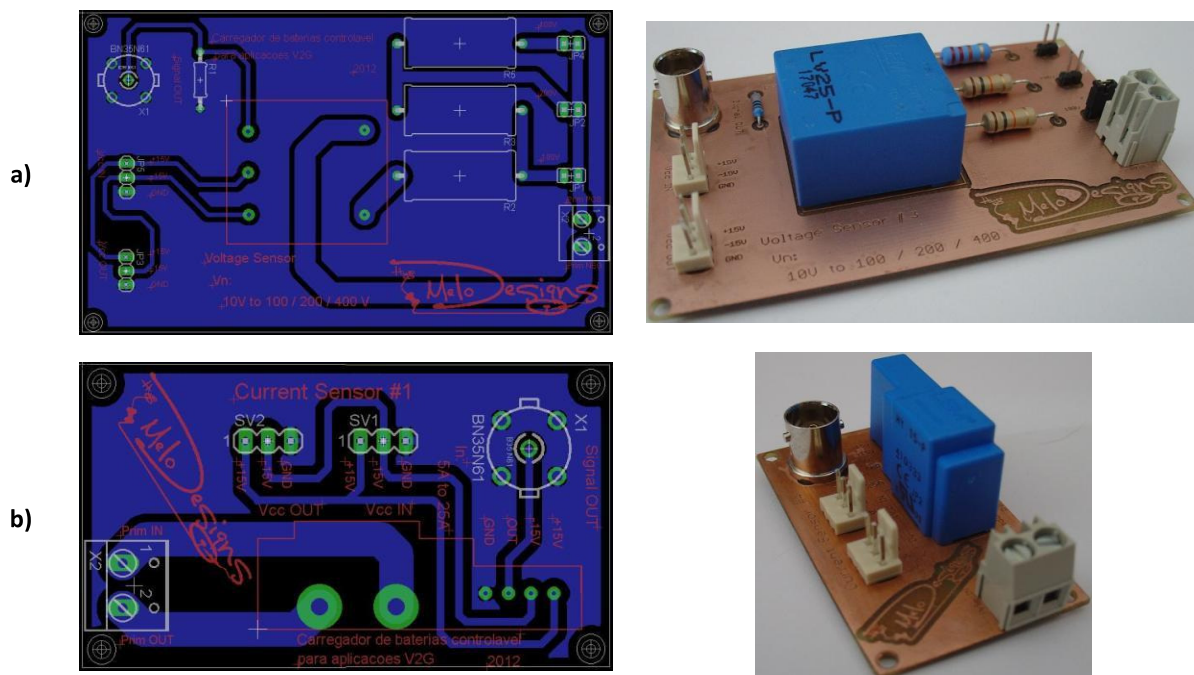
a) *Layout* do PCB para condicionamento do sensor de tensão e respectiva imagem real do mesmo assembled. b) *Layout* do PCB para condicionamento do sensor de corrente e respectiva imagem real do mesmo assembled.
